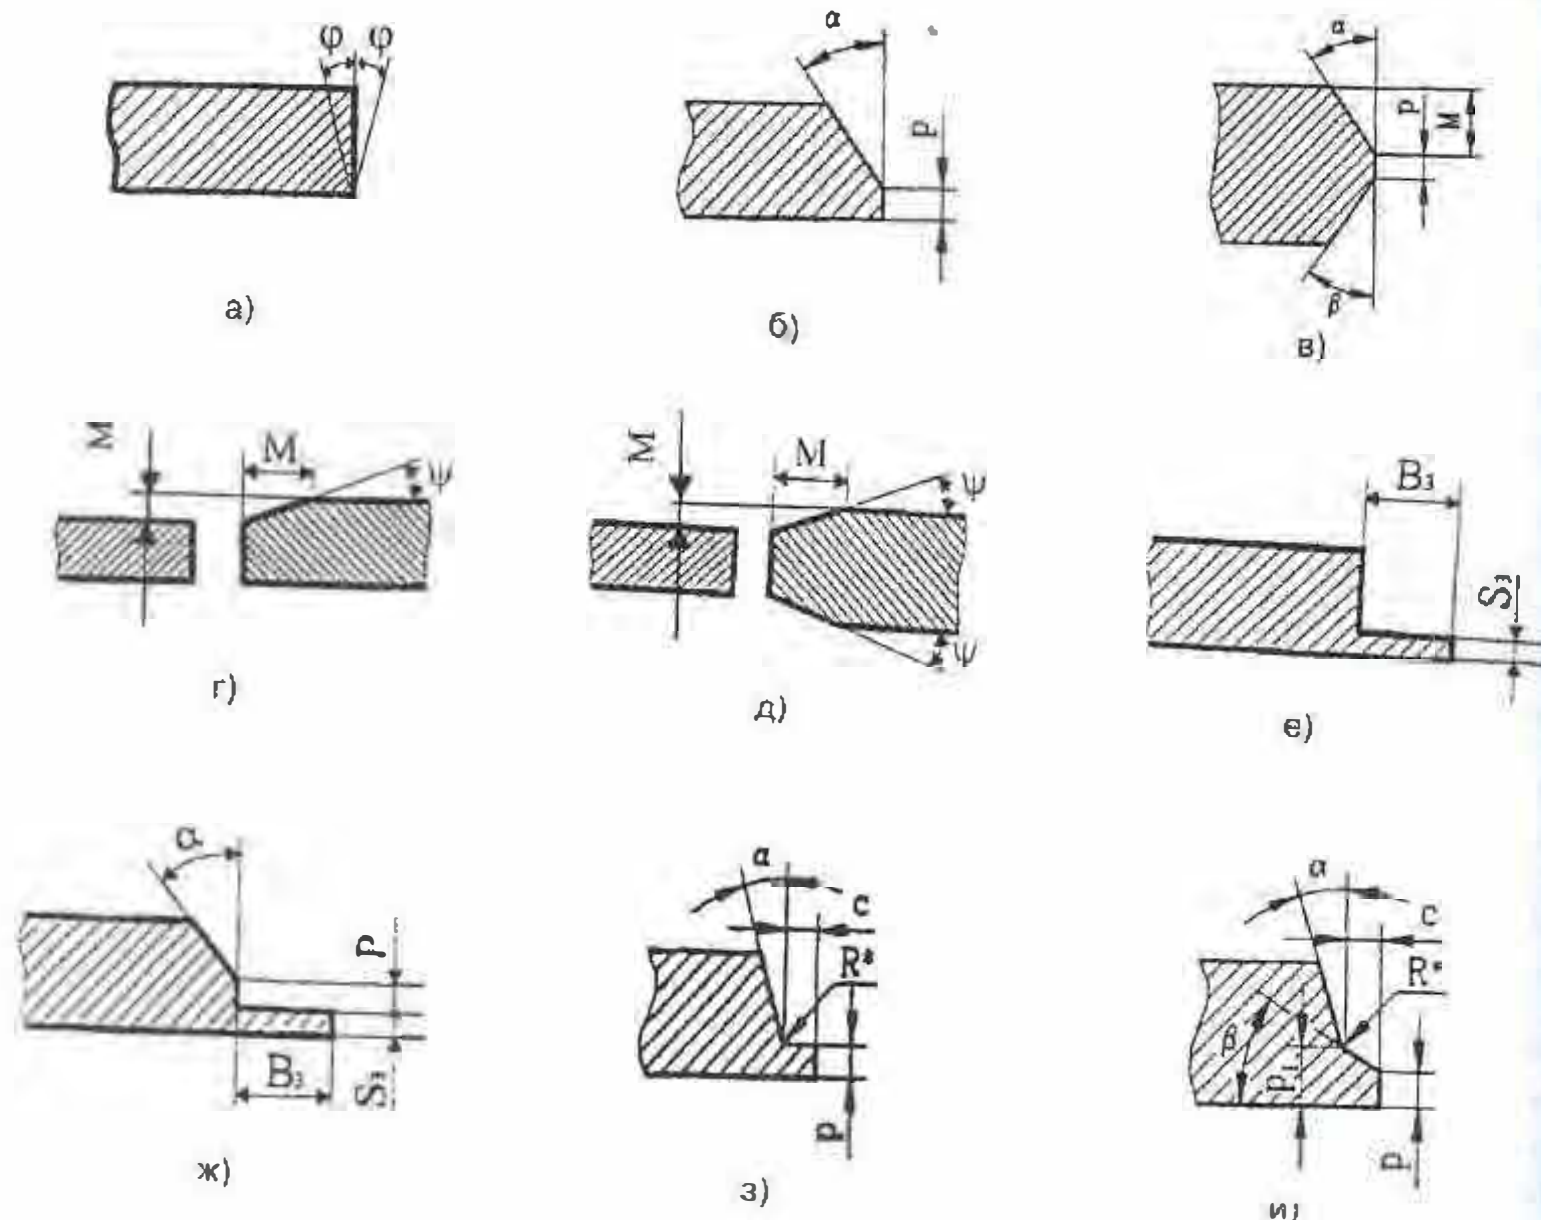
лист 1. Размеры, контролируемые измерением при подготовке деталей под сварку
